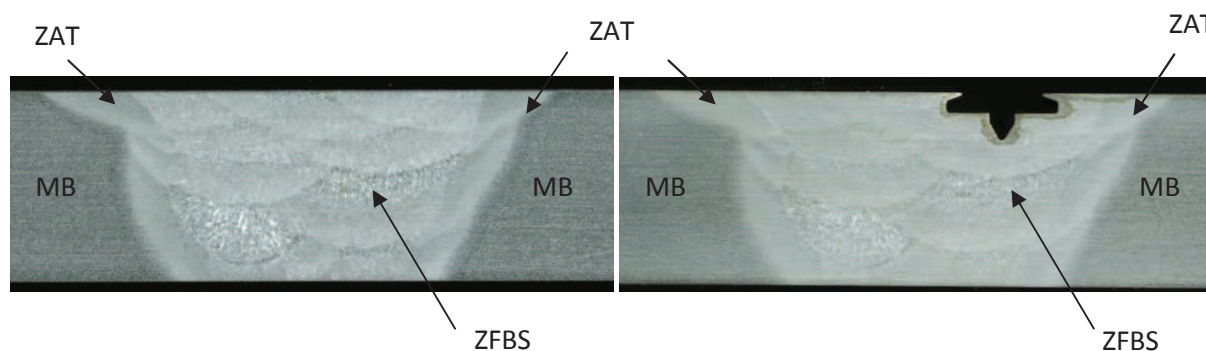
Soudure attaquée en cours d’usinage (gauche) et entaille usinée au-dessus d’une ZFBS (droite)
